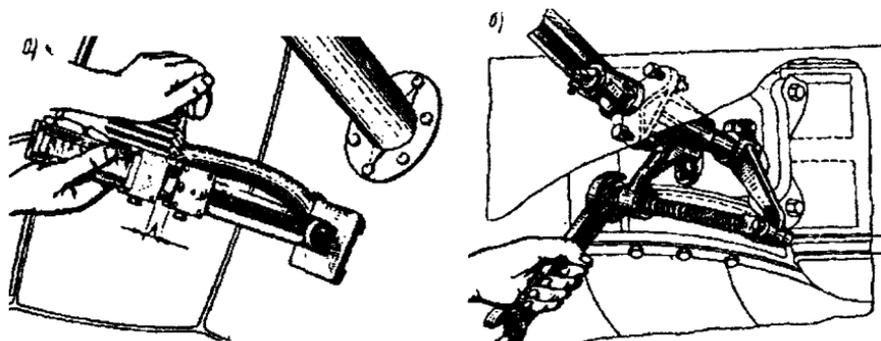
Регулировка свободного хода педали сцепления автомобиля ЗИЛ:
